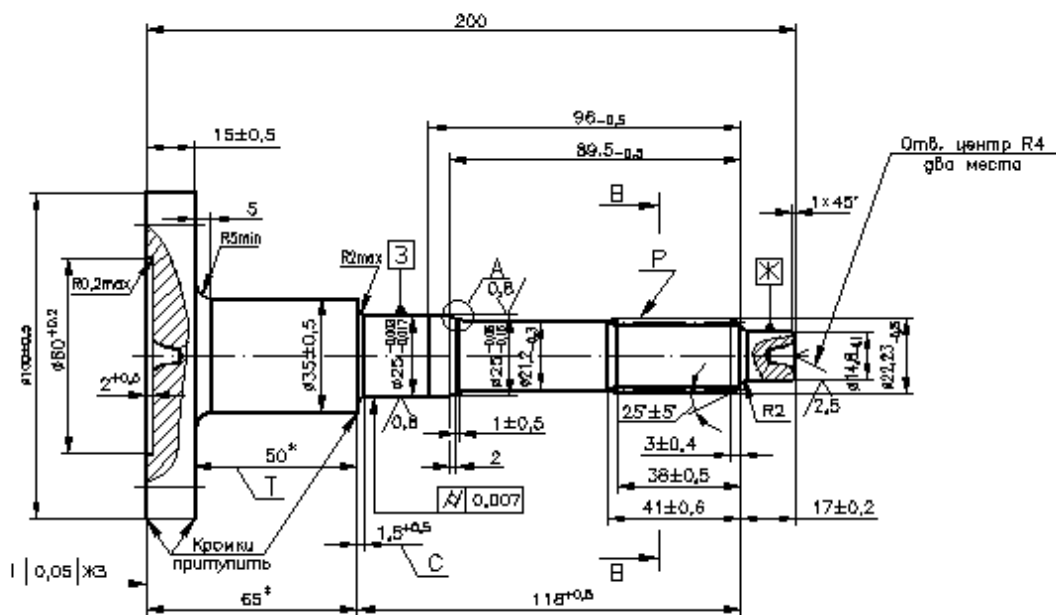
Рабочий чертеж передаточного вала от двигателя к карданному валу
